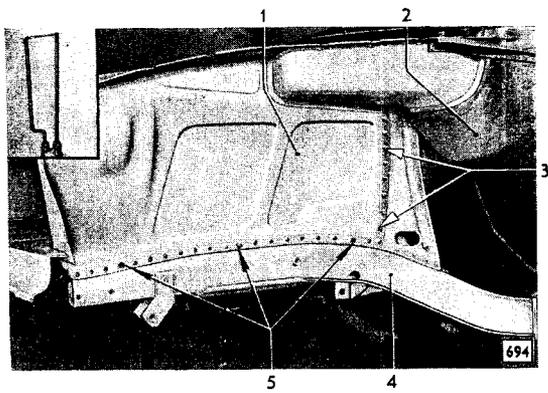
Radeinbau an Stirnwandstütze und an Vorderrahmenlängsträger punktgeschweißt
